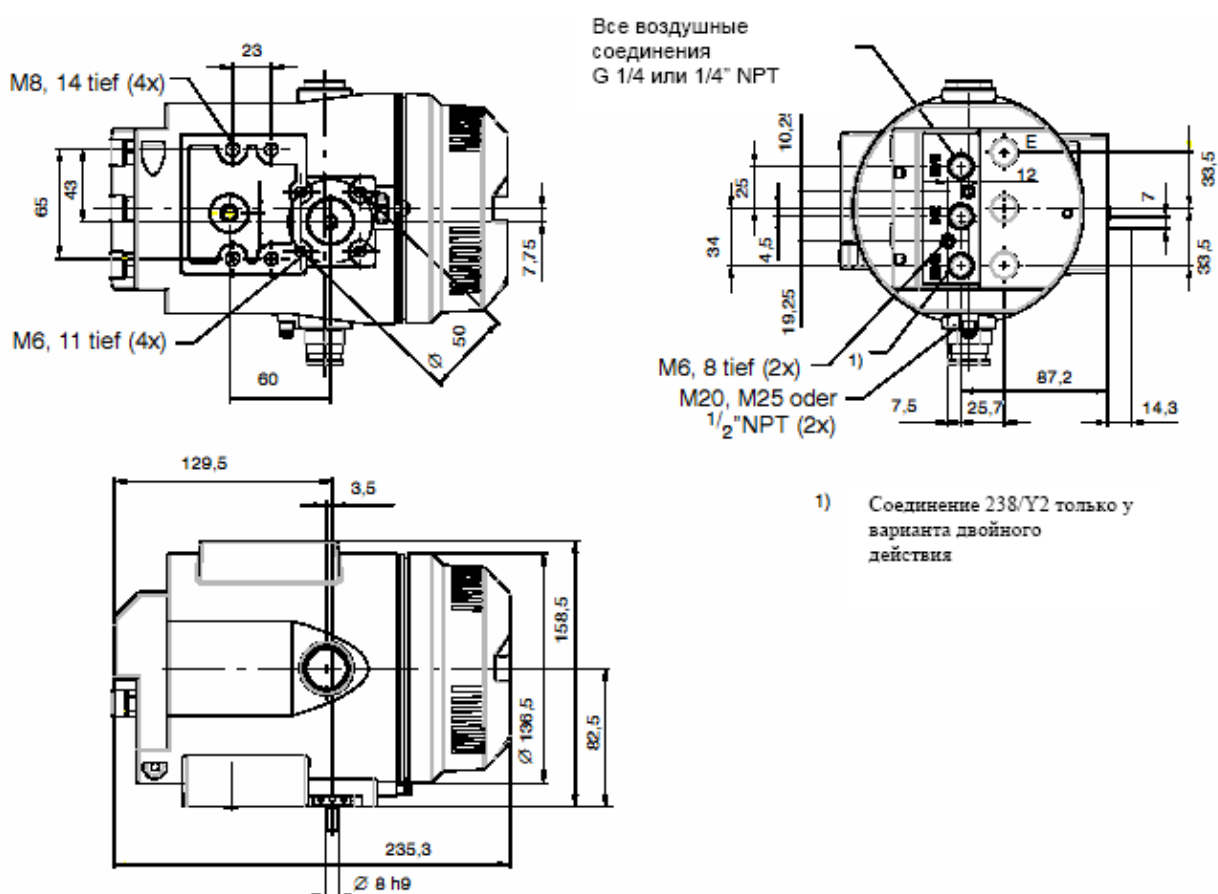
Габаритный чертеж позиционера в металлическом корпусе со взрывонепроницаемой конструкцией 6DR5xx5
